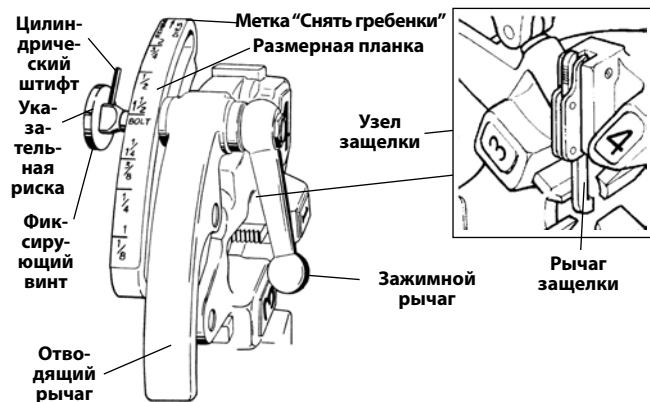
Универсальная самооткрывающаяся резьбонарезная головка
